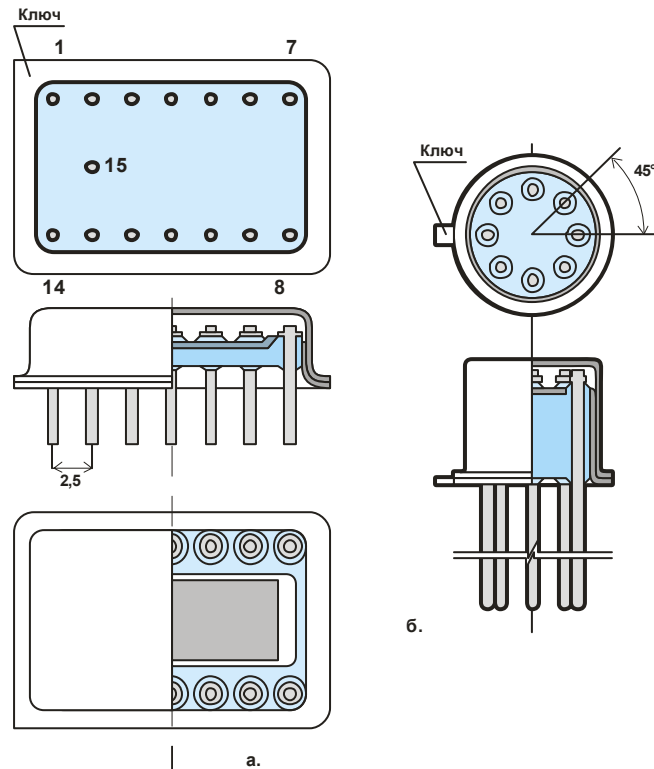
Конструкція металоскляних корпусів: а - підтипу 1203; б - підтипу 3104
